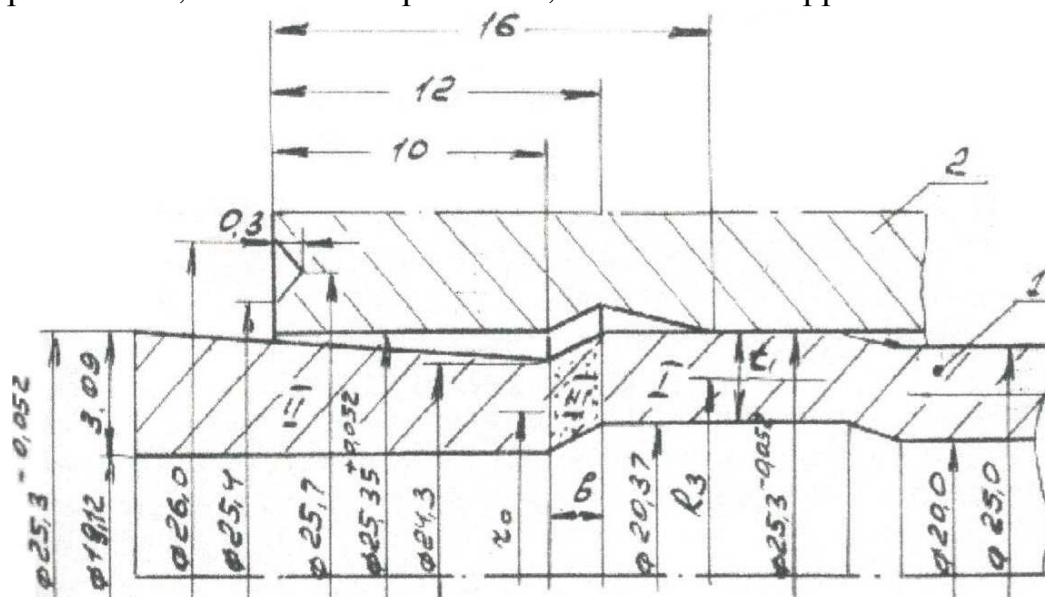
Сборка профилированной законцовки трубы с трубной решеткой
